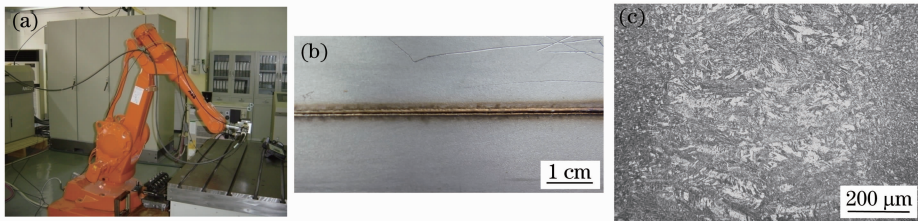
焊接设备及焊缝形貌。(a) 焊接设备;(b) 焊缝表面;(c) 焊缝截面
